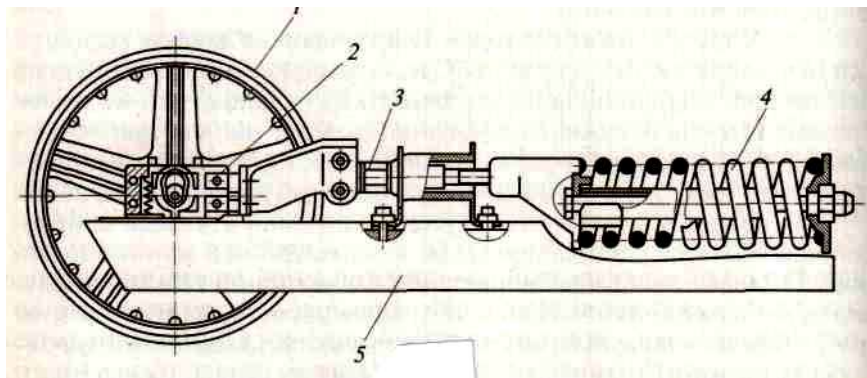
Схема установки направляющего колеса на ползуне:
